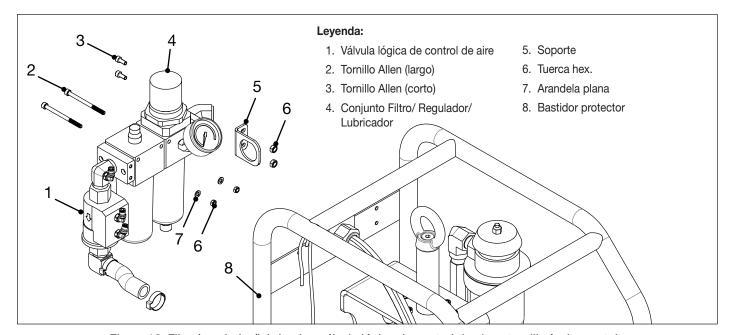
Filtro/regulador/lubricador, válvula lógica de control de aire y tornillería de montaje
